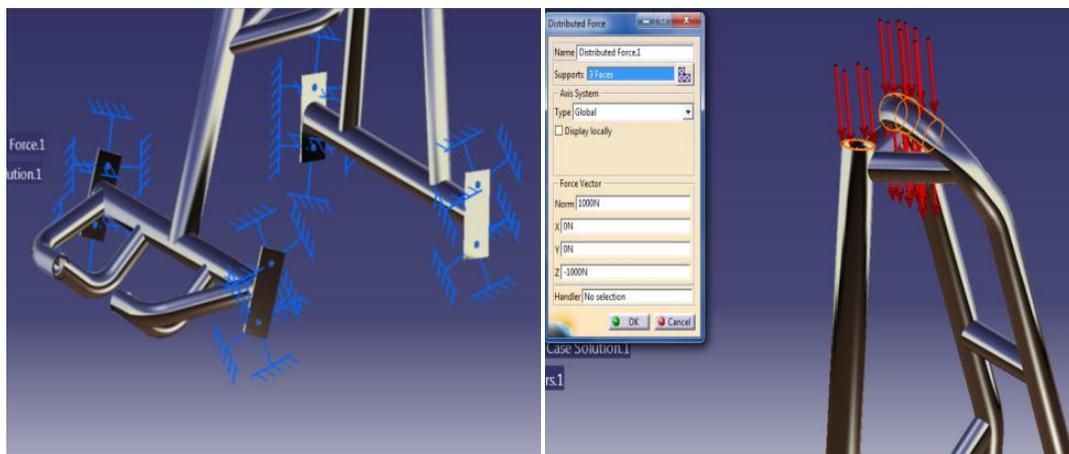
Asignación de cargas y restricciones en la estructura superior.
